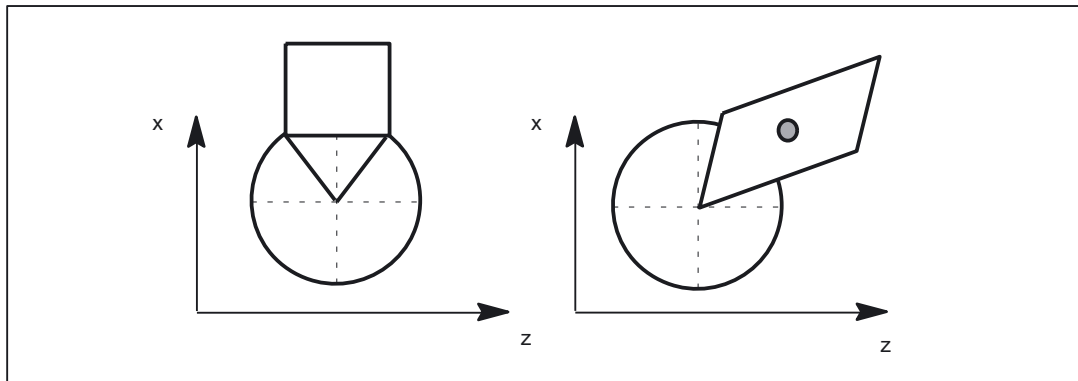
Messen von Werkzeuglängen mit Lupe
